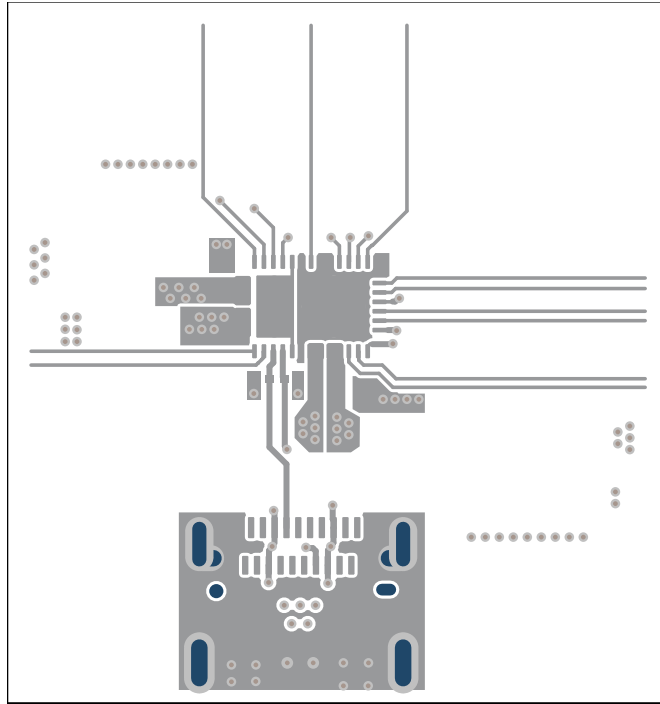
TPS25751D PCB Layout - Top Layer Routing
